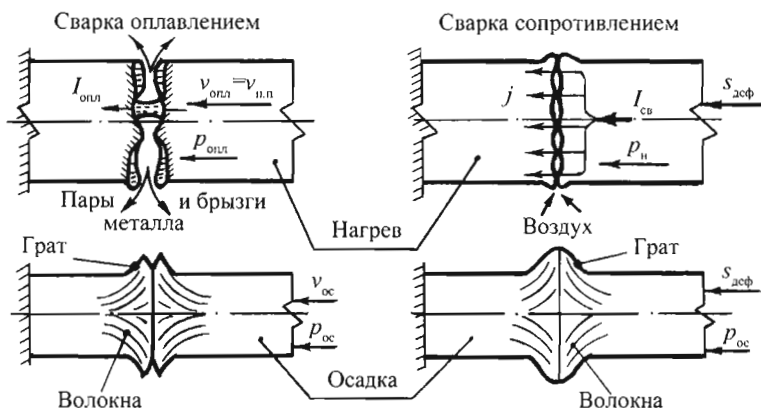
Схема процесса стыковой сварки:
